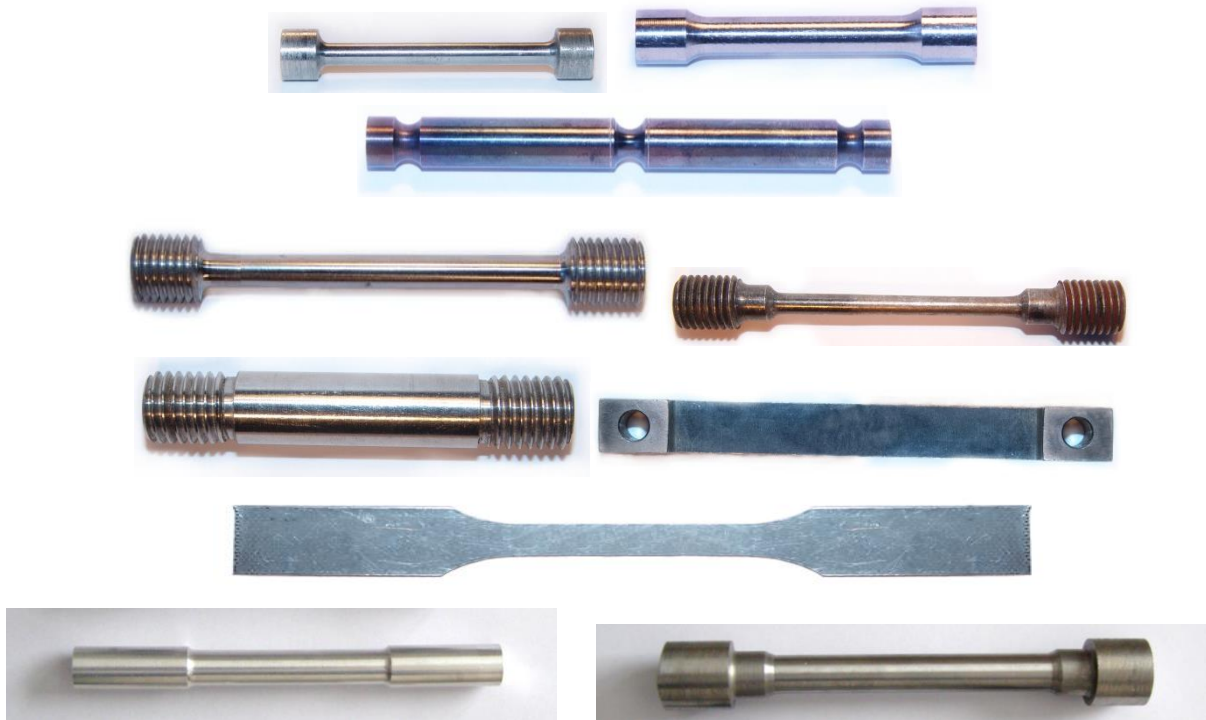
Зразки для механічний випробувань з захватами різної форми.
